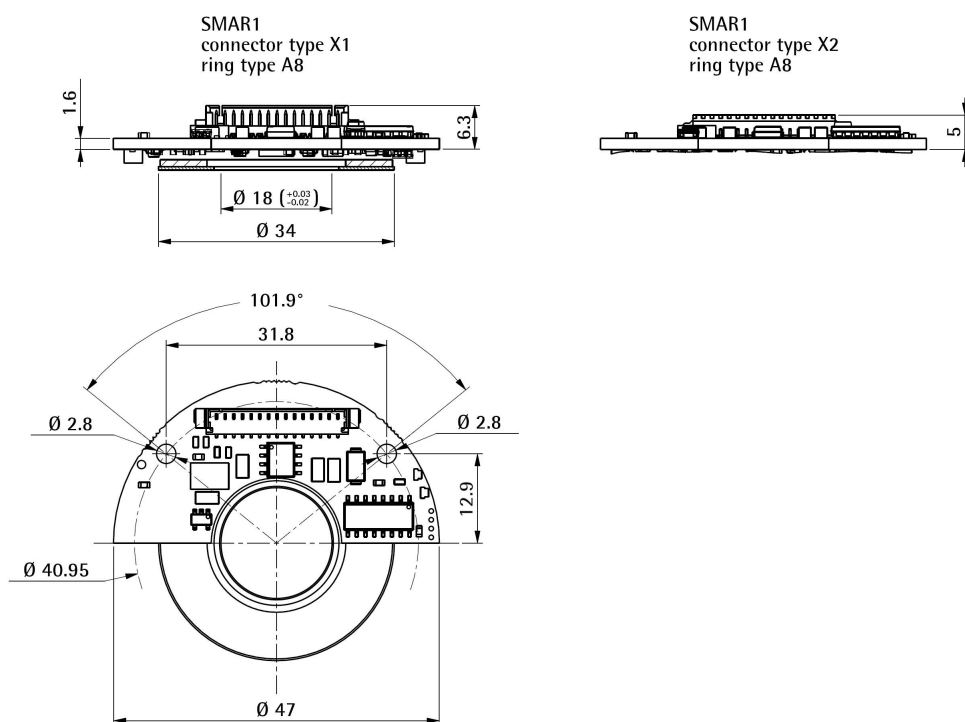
SMAR1 + MRA34A senza supporto di montaggio meccanico
